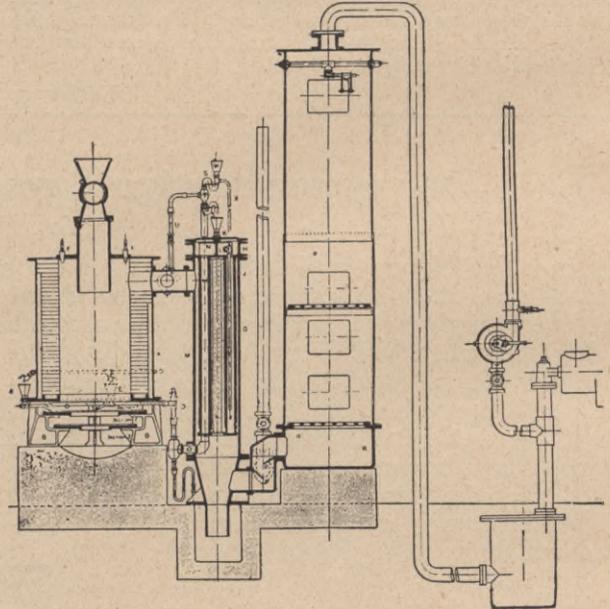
Schnitt durch einen Crossley-Sauggaserzeuger.
